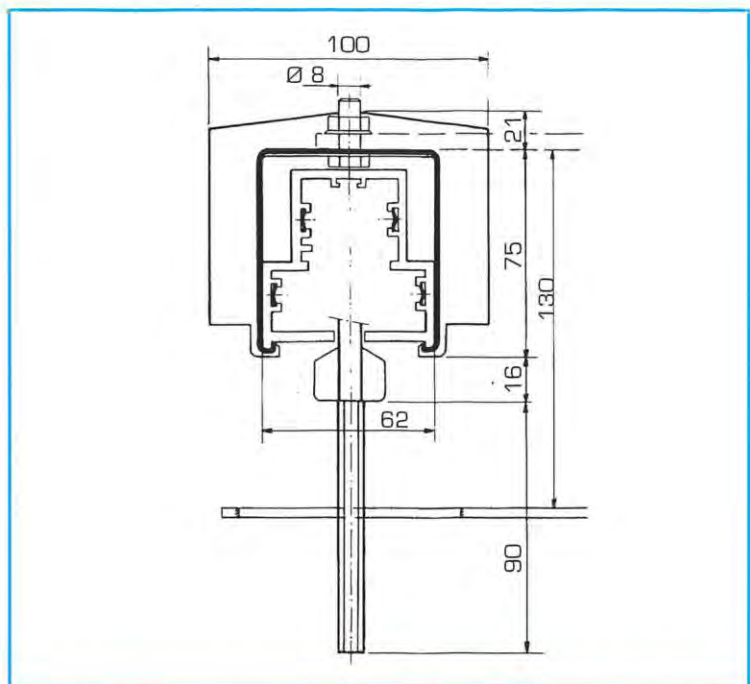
Seitenansicht vom Stromabnehmer CC 430, Mitnehmer ED 32 Aufhängung CA 206.
